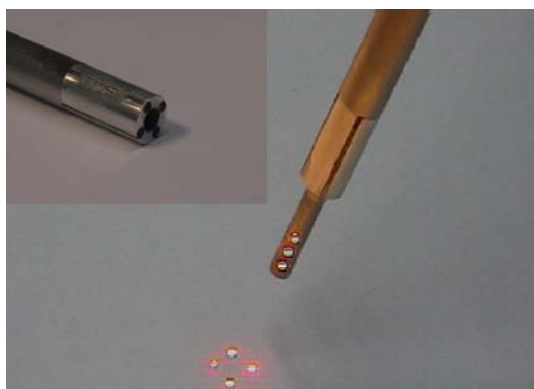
(a)-(b) prototype du porte outil à pointage laser
